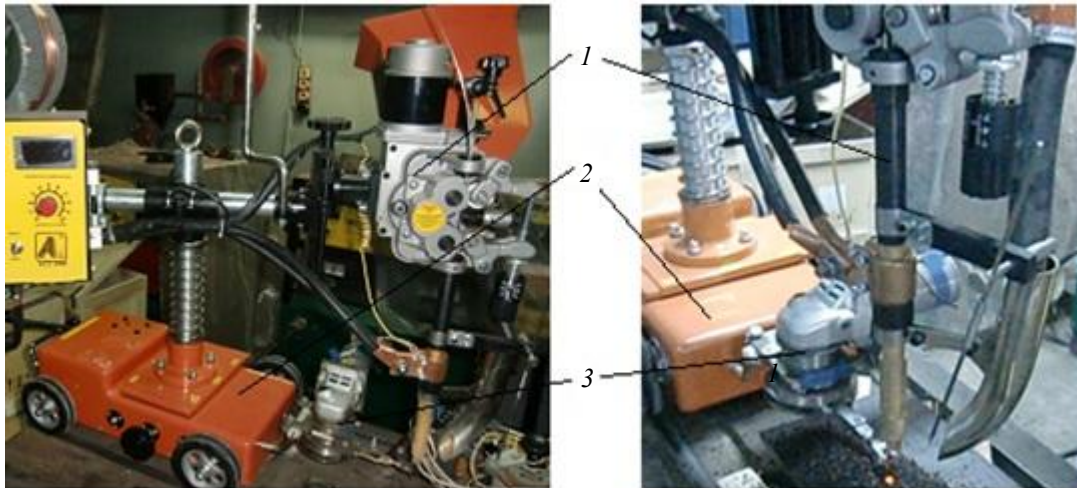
Сварочный трактор с механическим генератором для импульсного воздействия на электродную проволоку: 1 – сварочная головка; 2 – каретка трактора; 3 – механический генератор
